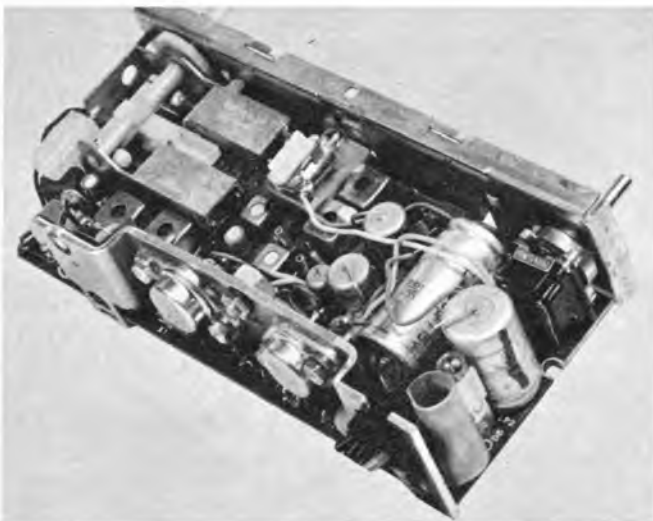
Innenansicht des Autoempfängers Solingen zum Selbsteinbauen (Aufnahme: Blaupunkt)
